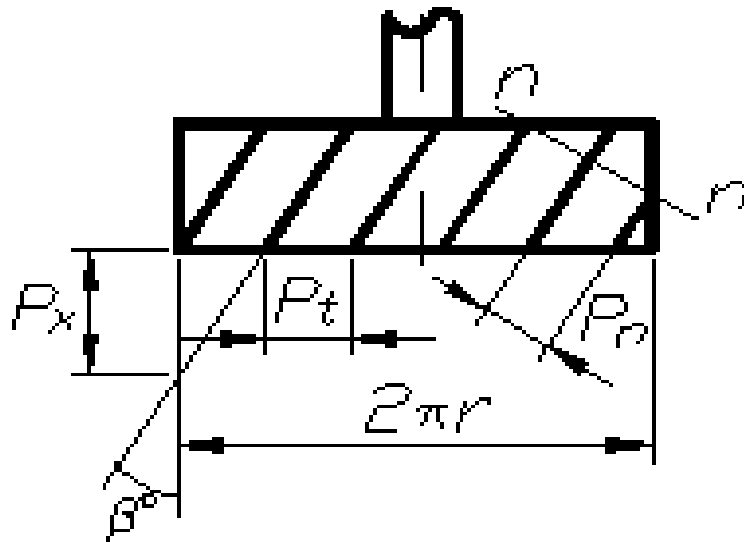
Кроки зубів косозубого колеса: p_x – осьовий;
